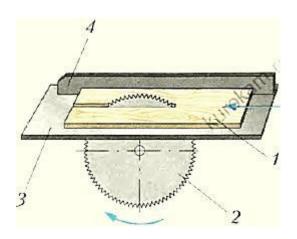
Схема обработки заготовки из древесины на круглопильном станке: 1— заготовка; 2— круглая пила; 3— стол станка; 4— упор
